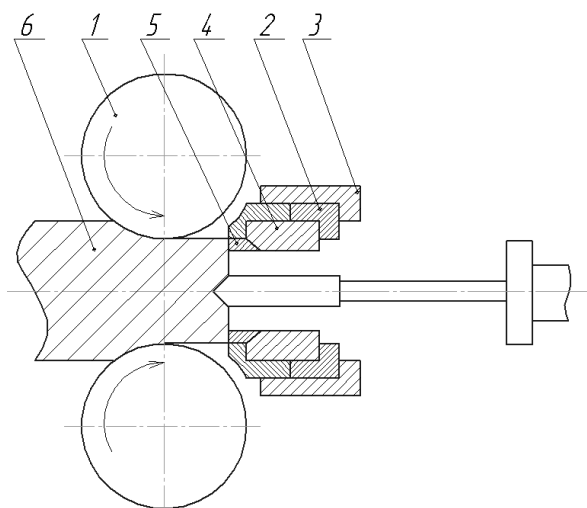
Схема устройства на стадии обжатия заготовки и центрирования пресс-иглы: 1 – прокатный валок; 2 – матрицедержатель; 3 – упор матрицедержателя; 4 – матрица; 5 – смазочная шайба; 6 – заготовка
